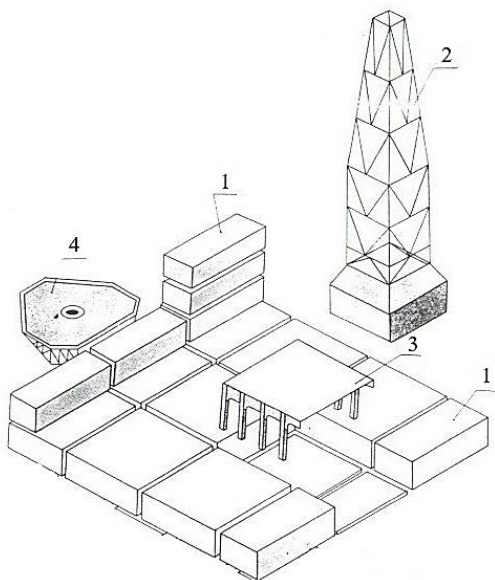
Разбивка конструкций ППБУ на сборочно-монтажные единицы (верхняя часть):
